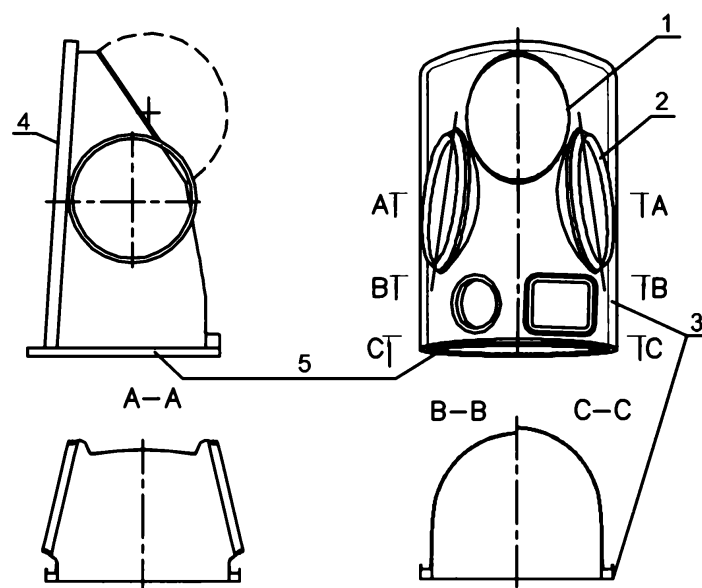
Вариант концепции оболочки жесткого корпуса: 1 — отверстие для шлема; 2 — отверстие для плечевого подшипника; 3 — рамка входного люка; 4 — входной люк; 5 — интерфейс между корпусом и нижней частью оболочки
